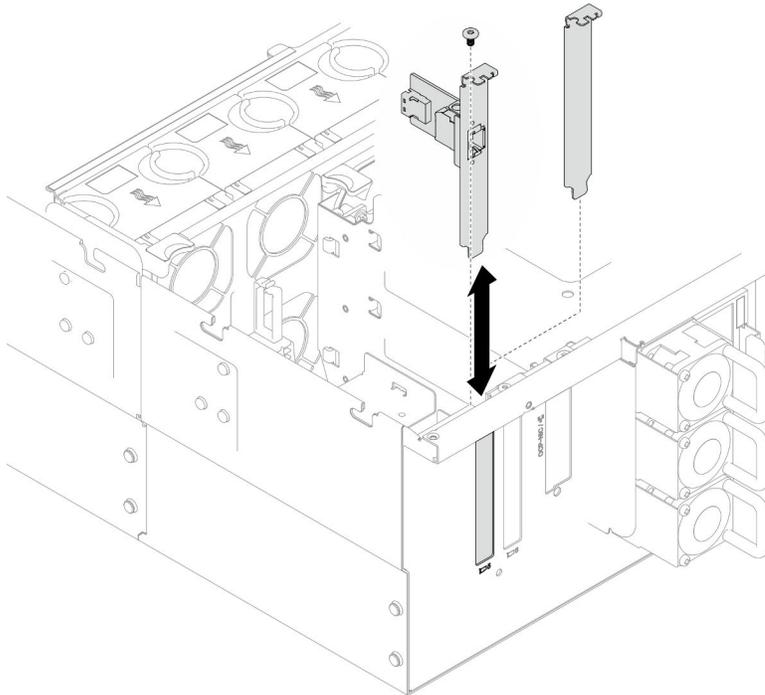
Installieren der Ethernet-Anschlussbaugruppe
